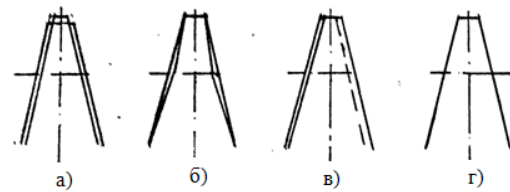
Схема профильного формообразования зубьев реек: а – прогрессивная схема формообразования с чередованием вершинных и профильных зубьев инструмента; б – прогрессивная схема формообразования с чередованием вершинных и профильных зубьев инструмента с «протуберанцем»; в – прогрессивная схема формообразования с чередованием профильно-вершинных односторонних зубьев инструмента с левым и правым профилями; г – контурный полный способ формообразования
